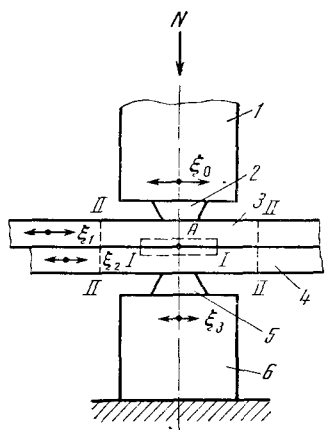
Схема точечной ультразвуковой сварки
